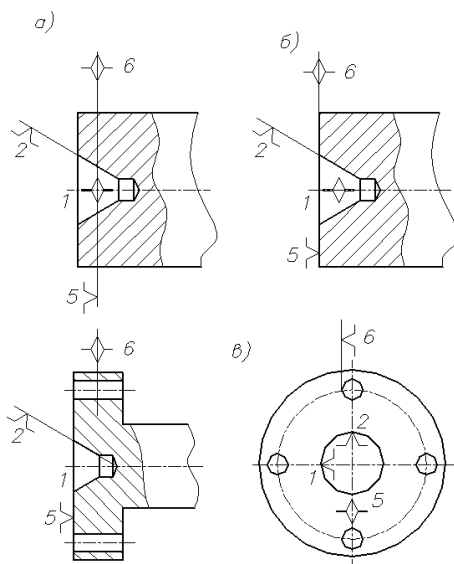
Теоретическая схема базирования при применении рифленого упорного центра (*а*), плавающего поводкового зубчатого центра (*б*) и плавающего поводкового штырькового центра (*в*)
